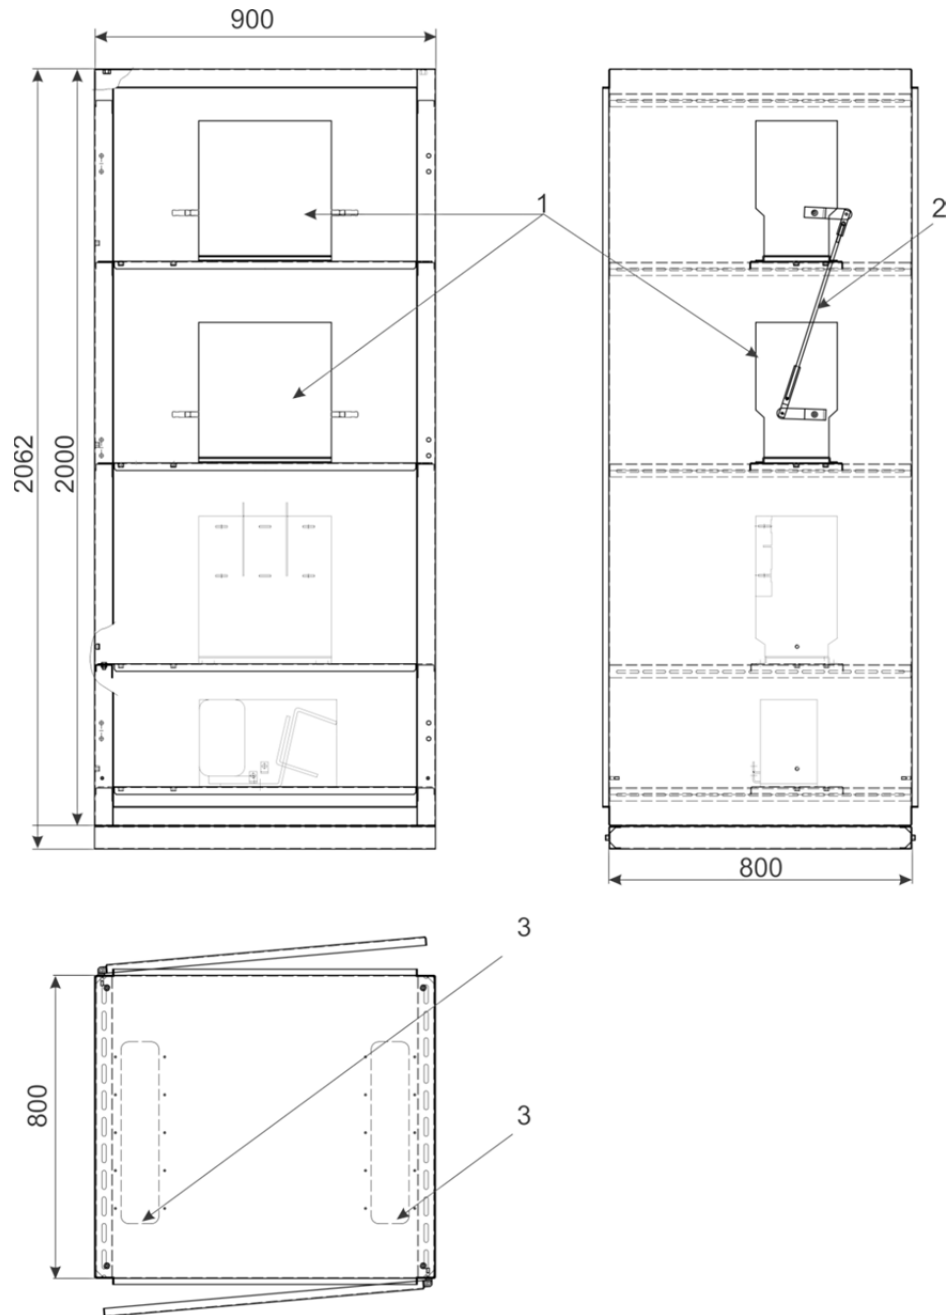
Габаритно-установочные размеры шкафа-реверсора
